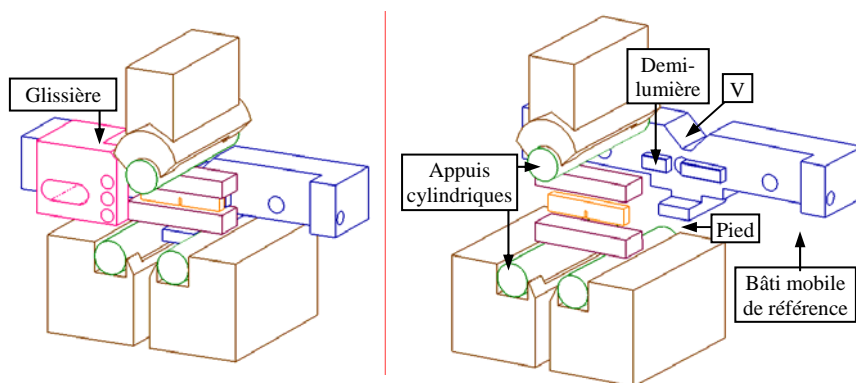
Montage utilisé pour la mise en place des poutres de l'essai SB
